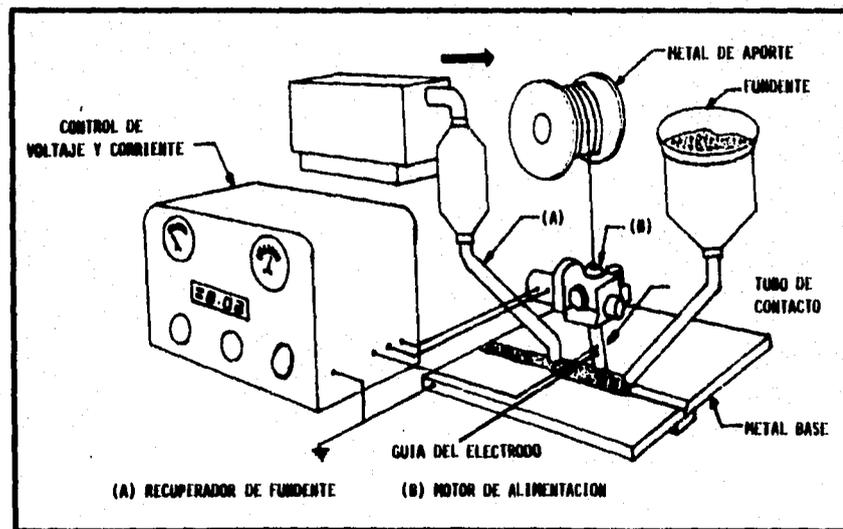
DETALLE DEL PROCESO DE SOLDADURA SAM.
